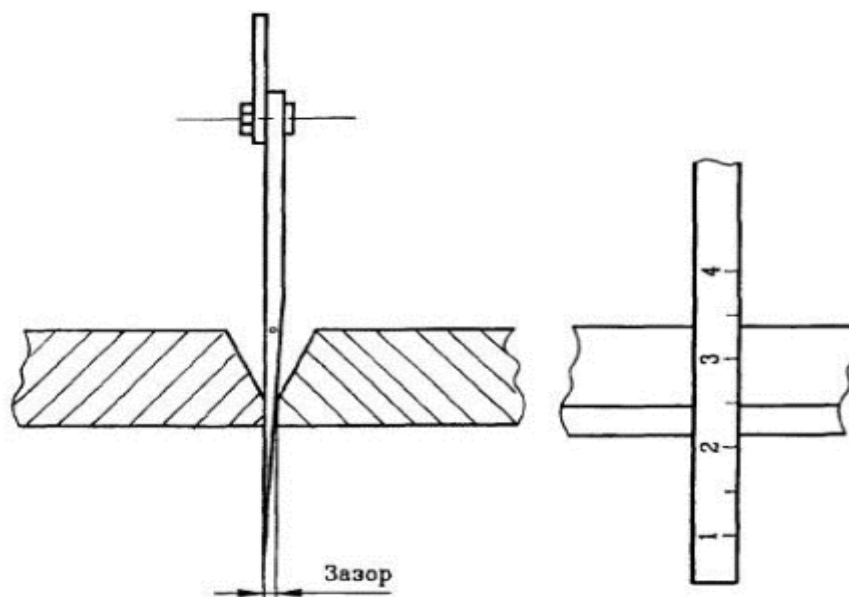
Схема измерения зазора сварного шва
